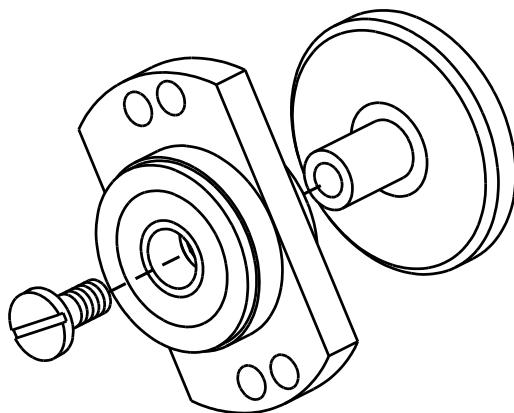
, Сборка фланцевого планетарного держател -шлифовального шпиндел
